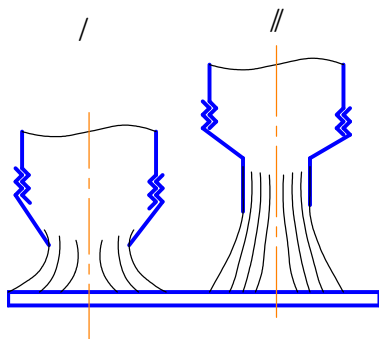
Форма сопел для сварки в среде защитных газов
